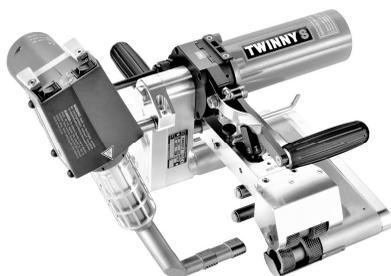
А. Сварочный автомат горячего воздуха «Twinny S»
